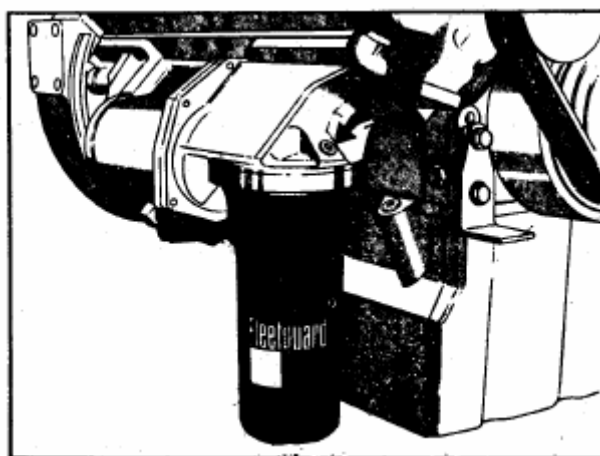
(OM1003L). Точка заливки системы смазки - двигатель V/VT-555 C.I.D
